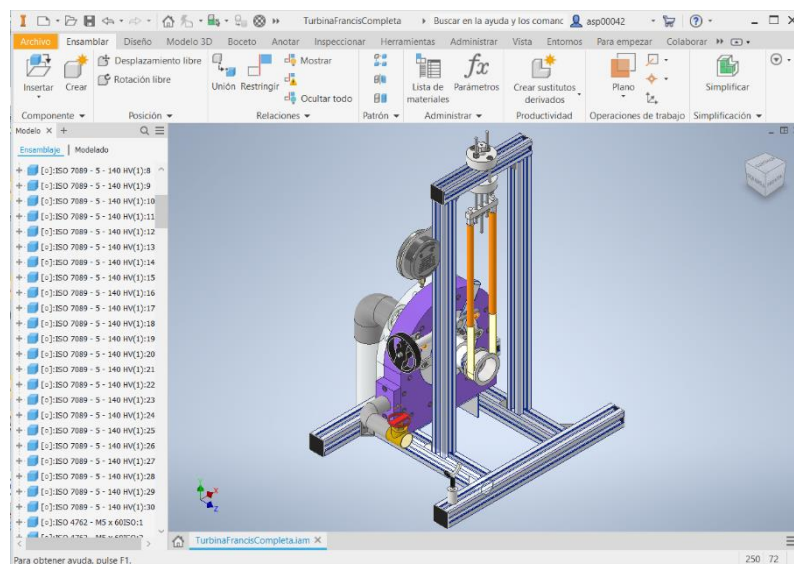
Diseño en Autodesk Inventor del conjunto Turbina Francis parte trasera.
